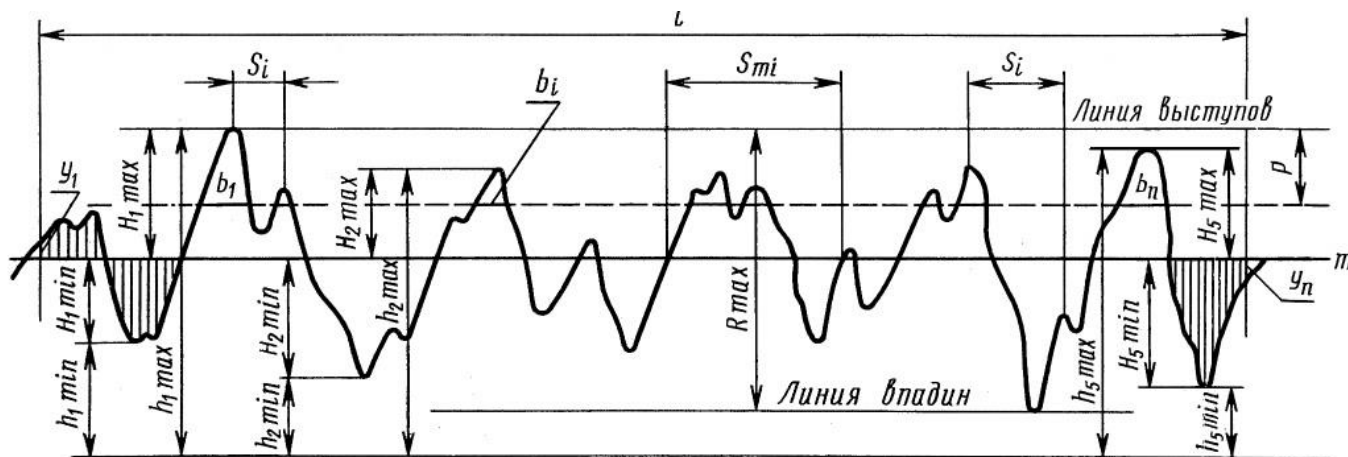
Параметры шероховатости поверхности вала/отверстия
